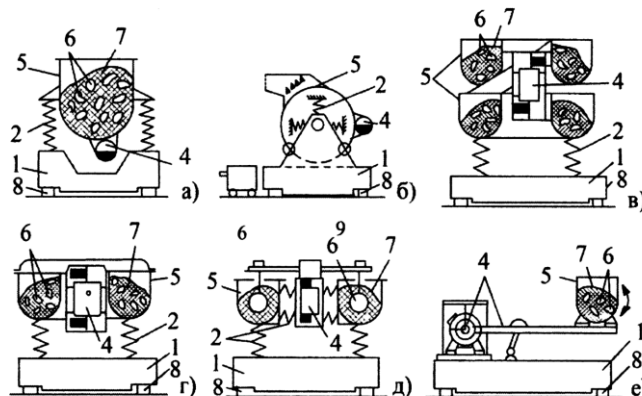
Схеми віброобробки деталей без закріплення: 1 - основа; 2 - пружні елементи; 3 - рухома рама; 4 - вібратор; 5 - контейнер; 6 - оброблювані деталі; 7 - інструментальне середовище; 8 - амортизатори; 9 - активатор коливань
